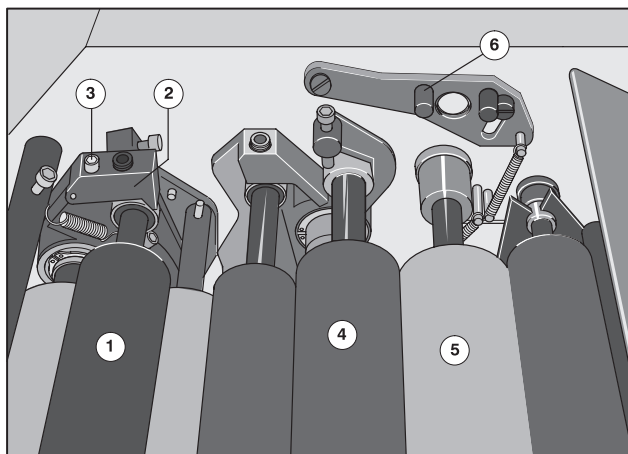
Установка 4-го передаточного валика и грузового раскатного валика
